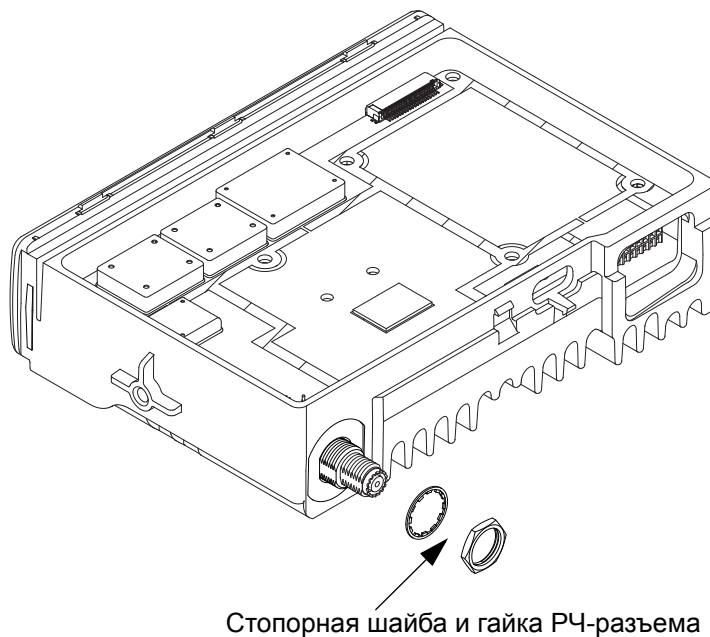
Вставка стопорной шайбы и гайки РЧ-разъема
